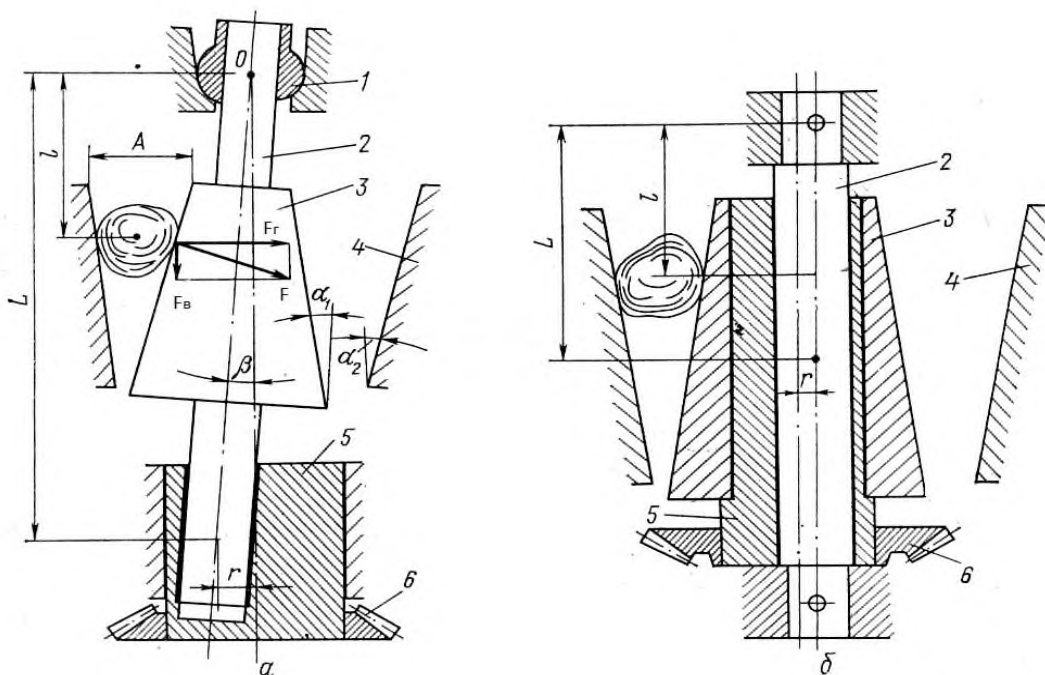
Схемы конусных дробилок для крупного дробления:
